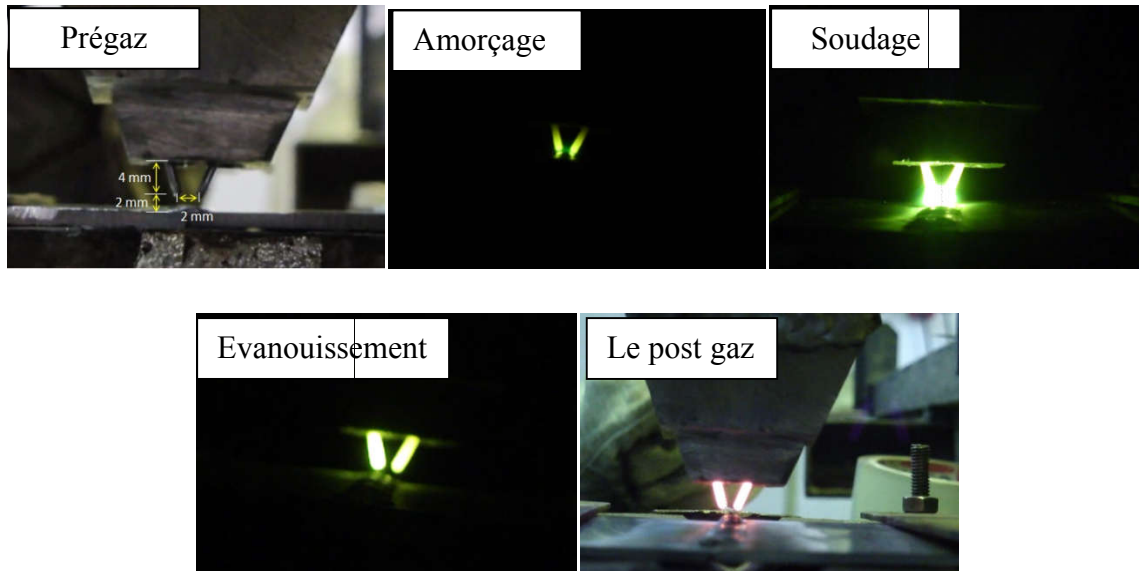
Cycle de soudage TIG double électrodes.
